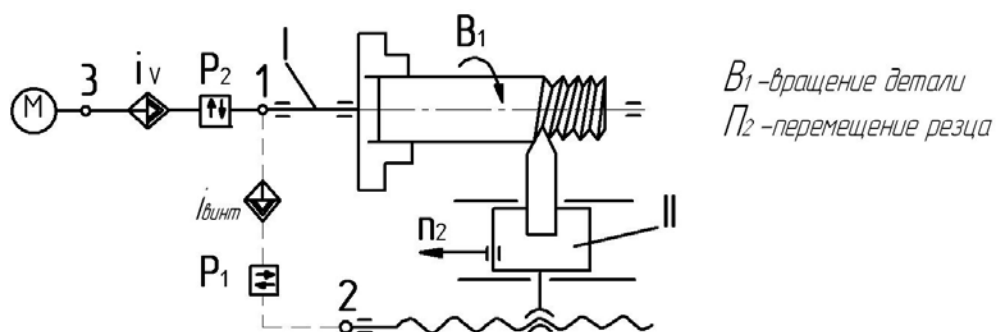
Структурная кинематическая схема токарно-винторезного станка
